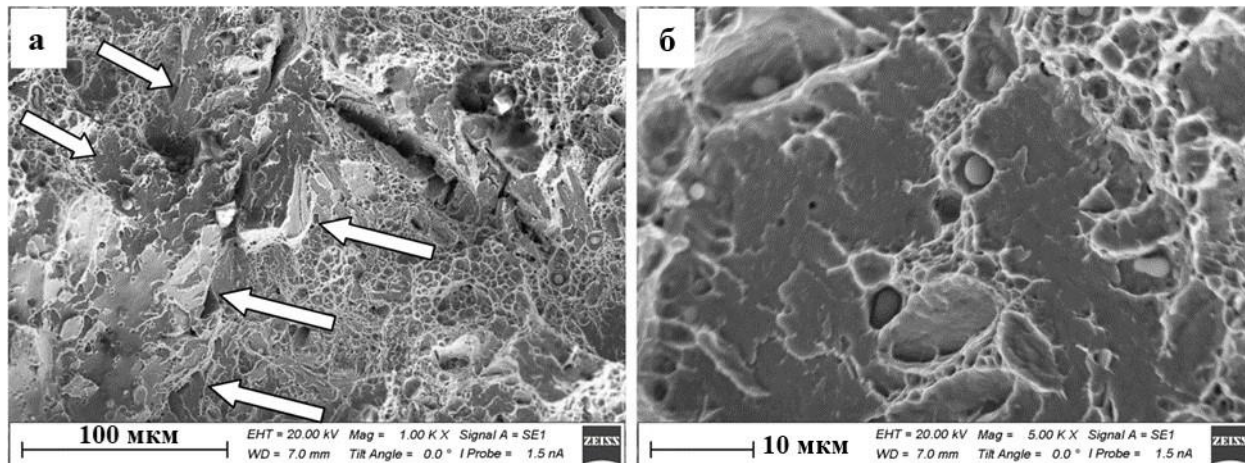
Структура поверхности разрушения металла наплавки (стрелками на (а) обозначена область квазихрупкого разрушения)
